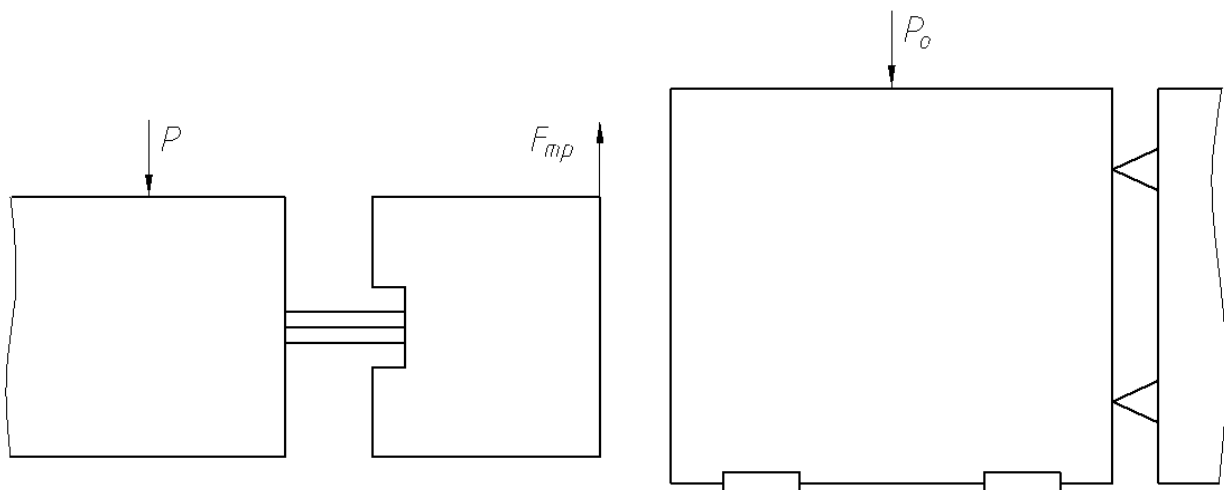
Розрахункова схема сил затиску заготовки
